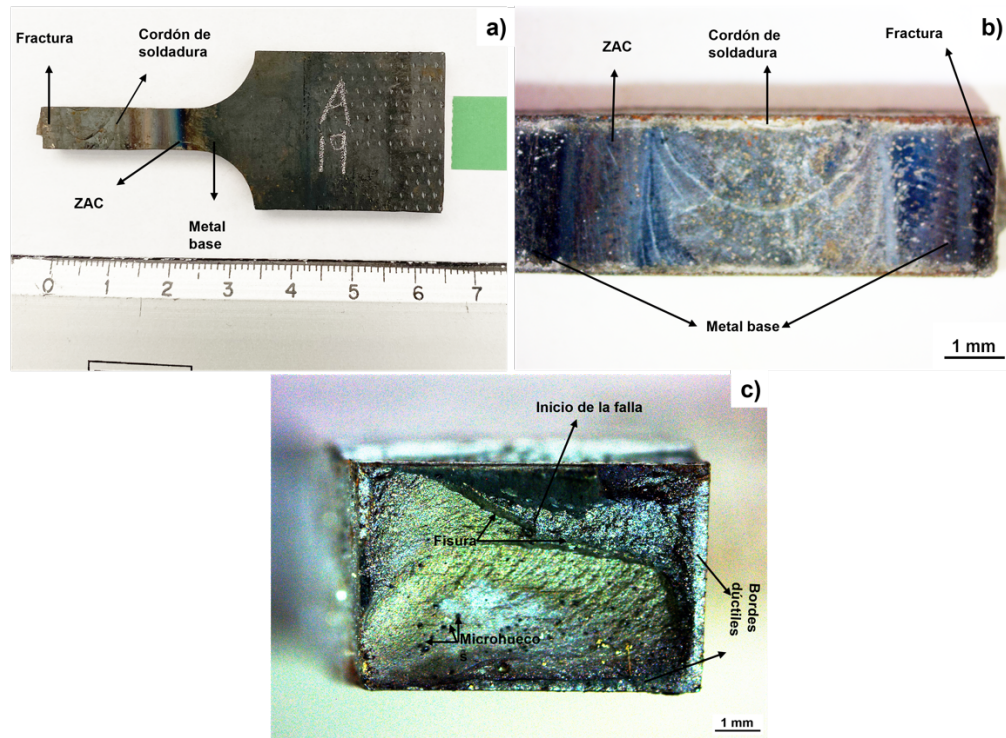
Fractografía estereoscópica para unión GTAW19A donde a) vista macroscópica con fractura en el metal base, b) vista longitudinal a 6.5x del cordón de soldadura al metal base, c) vista transversal donde se muestra fractura en el metal base.
